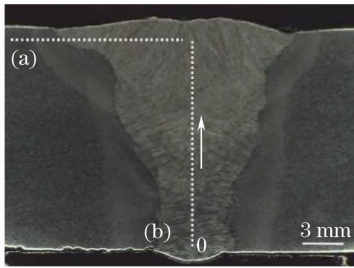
多层复合焊接接头宏观形貌。(a)表层焊缝硬度测量位置;(b)焊缝中心线硬度测量位置
